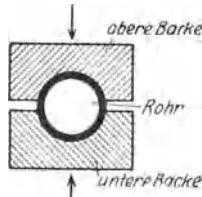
Klemmbacken für Rohrschweißung.
